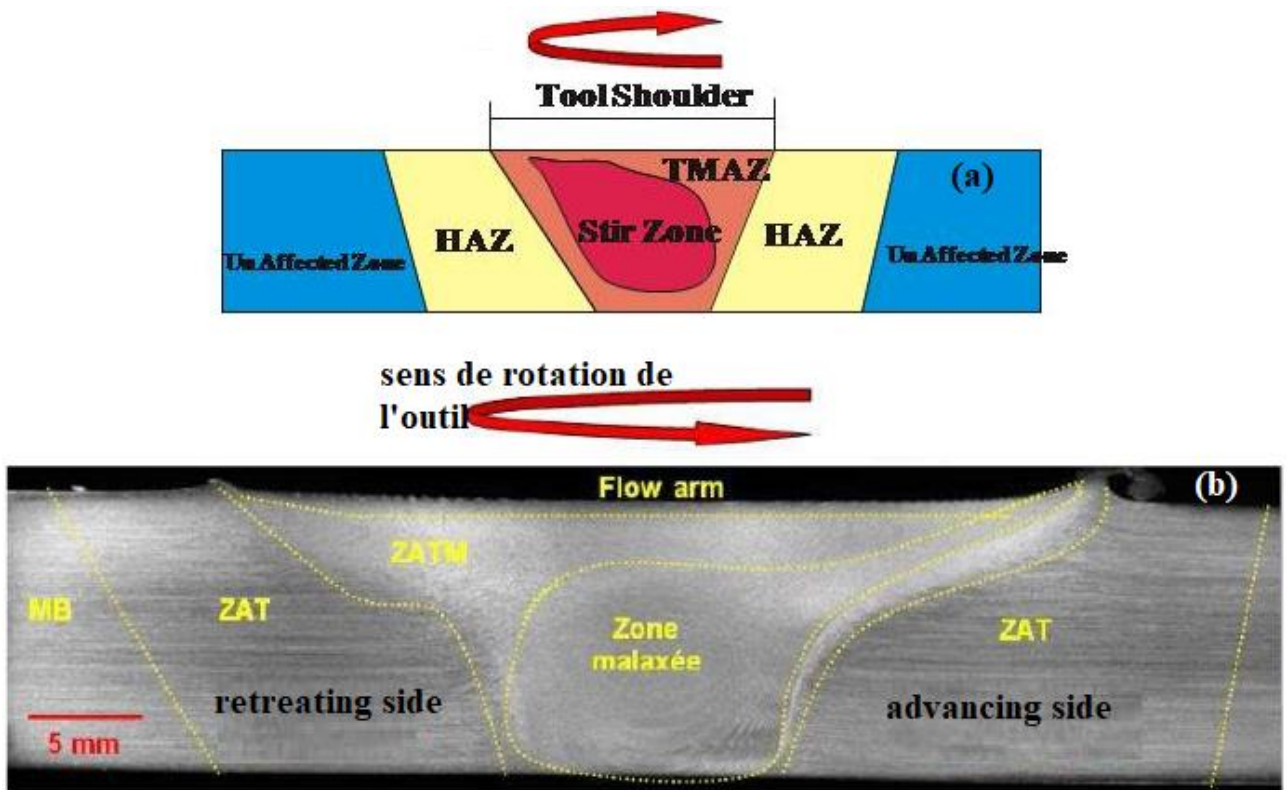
Structure macrographique d'un joint soudé par FSW [4]
